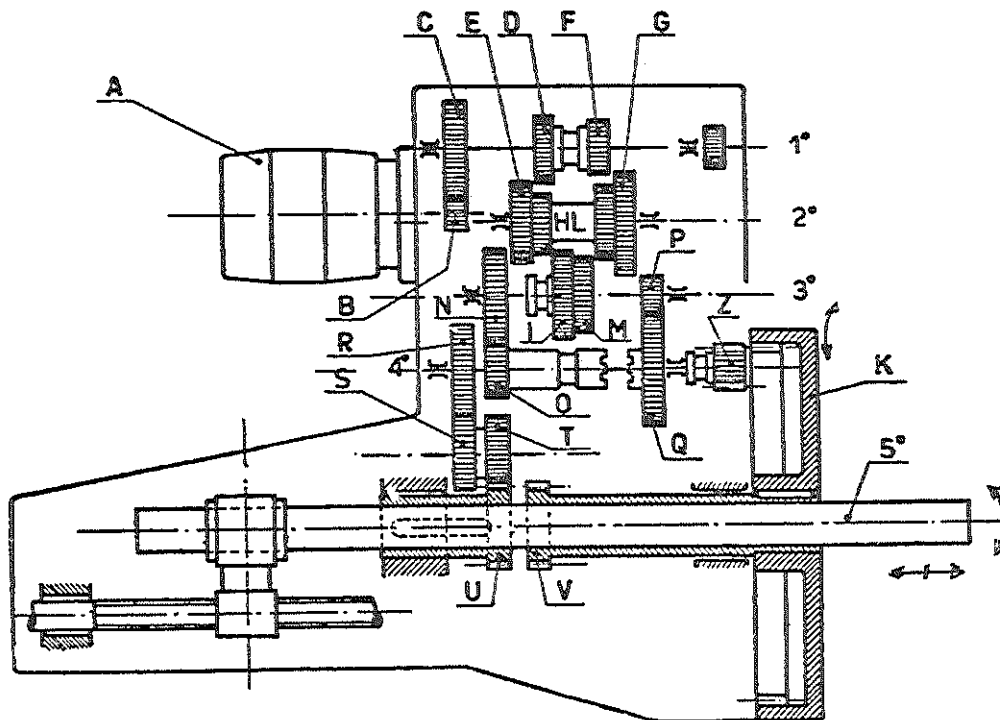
Esquema dos cinematismo de transmissão entre o motor e o mandril.
